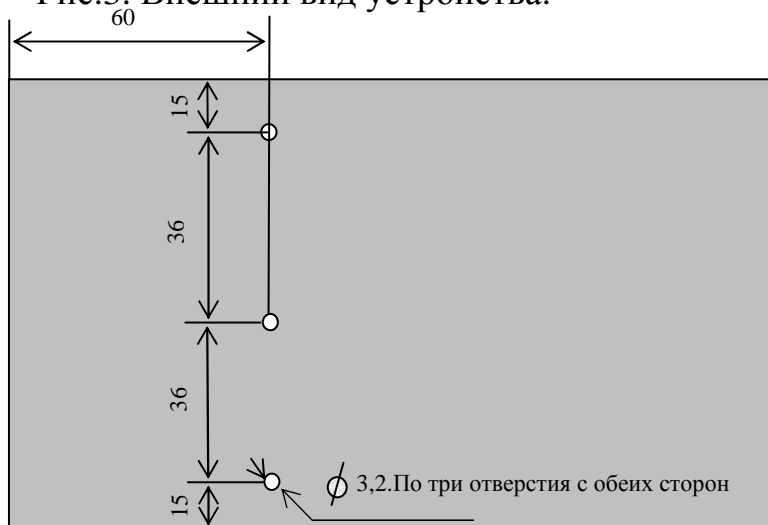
Расположение монтажных отверстий на боковых стенках корпуса.
